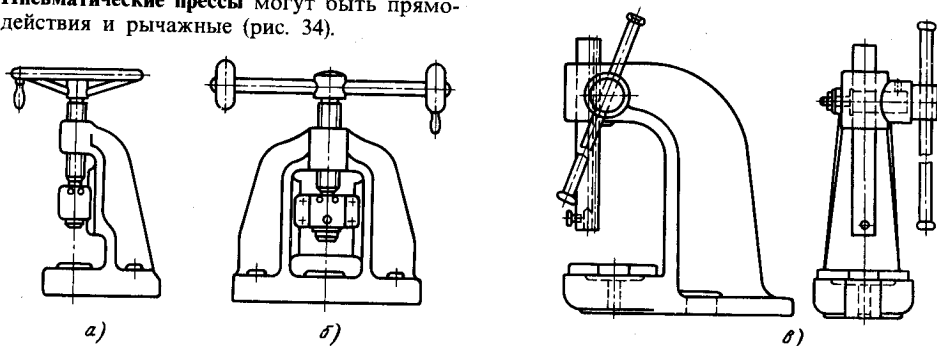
Ручные прессы: а - винтовой одностоечный; б - винтовой двухстоечный; в - реечный
